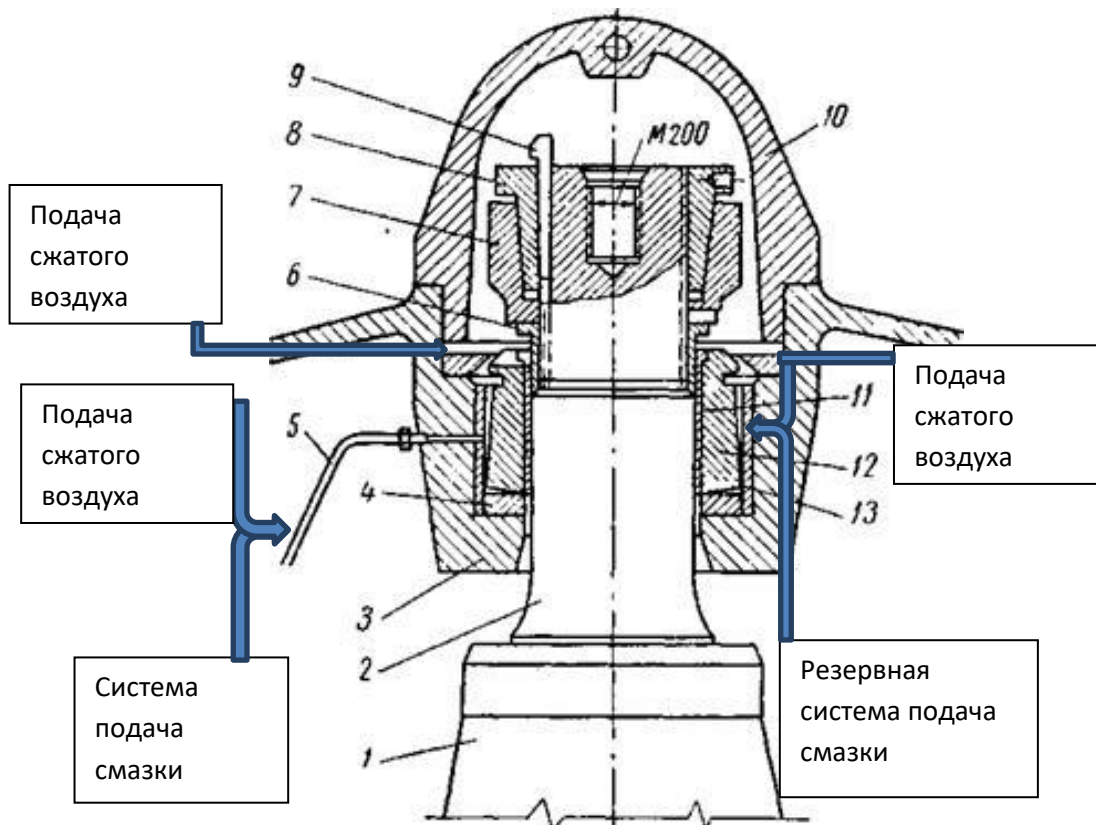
Верхний подвес конуса дробилки: I — дробящий конус; 2 — вал дробящего конуса; 3 — траверса; 4 — шайба; 5 — трубка для смазки; 6 — распорная втулка; 7 — обойма; 8 — разрезная гайка; 9 — клиновидная шпонка; 10 — колпак; II — втулка; 12 — конусная втулка; 13 — втулка
